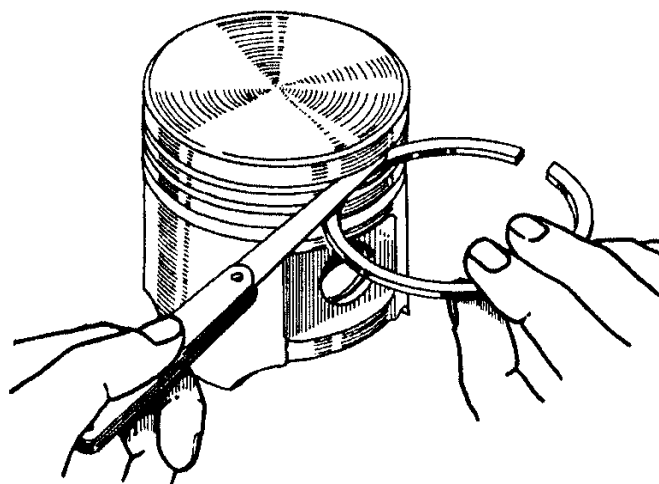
Проверка бокового зазора между поршневым кольцом и канавкой в поршне
